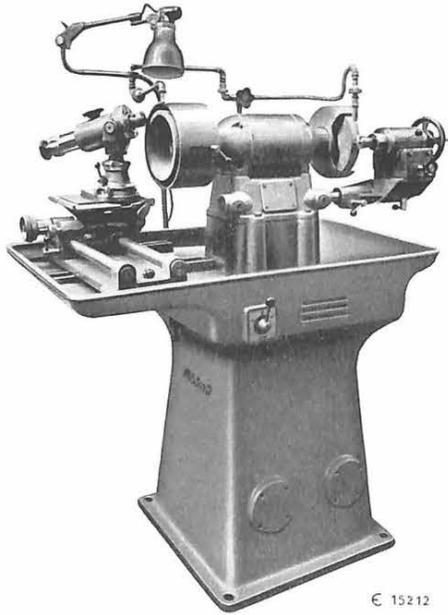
Affûteuse-meuleuse E 3 à meules en carborundum pour taillants en carbure de tungstène.
